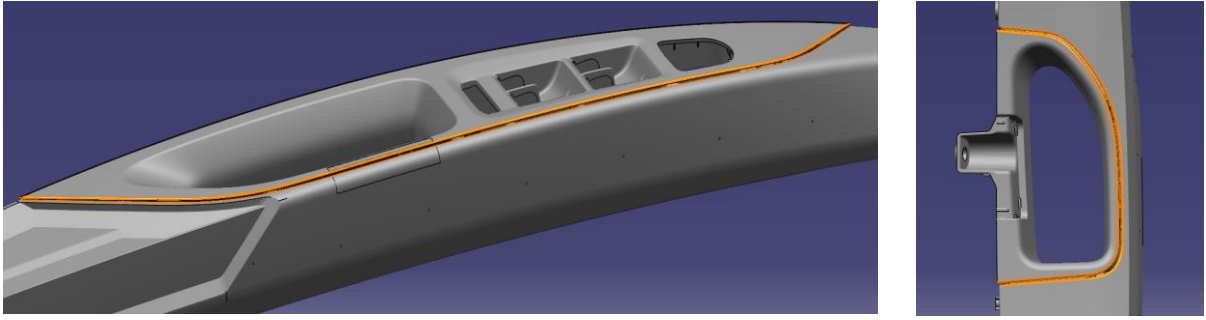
Zona de aplicación de la restricción (en naranja). Vista frontal / Vista por abajo
